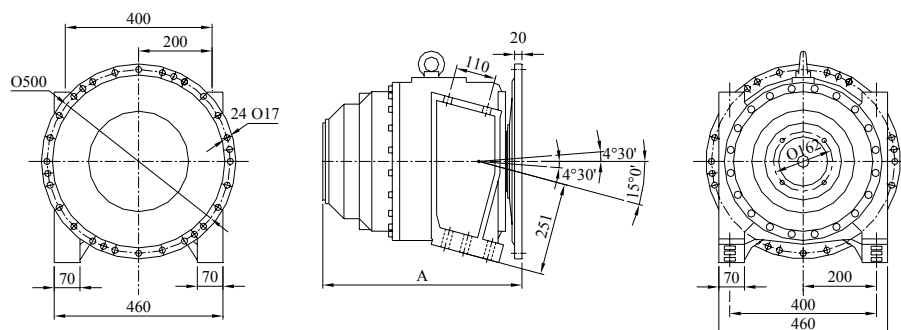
Редуктори Bonfiglioli Riduttori S.p.A. - Италия
